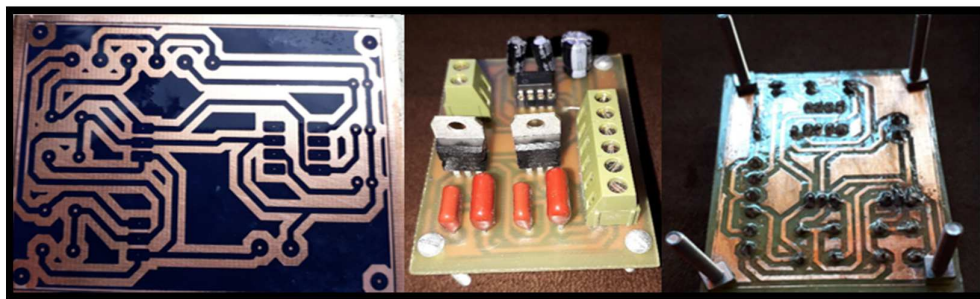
PCB fuente de alimentación -12v. Fuente: Autor
